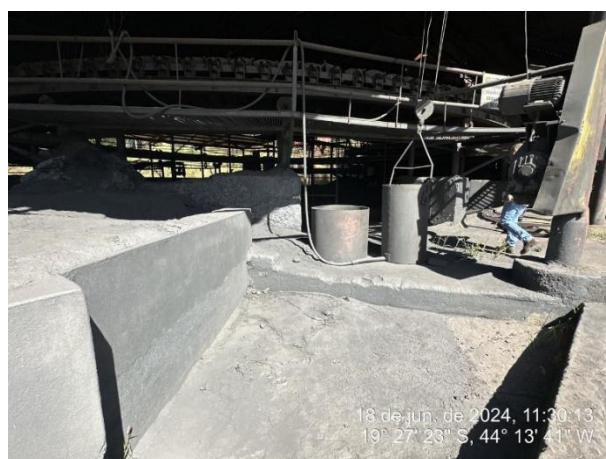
Local o qual armazenava grafite para lubrificar as lingoteiras
